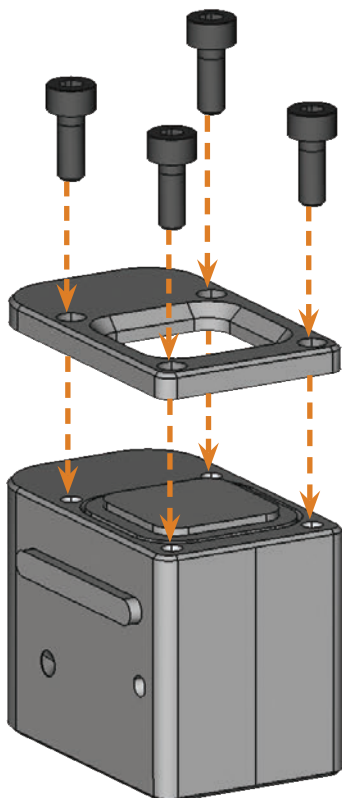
WERKZEUGMAGAZIN ZUSAMMENSETZEN
